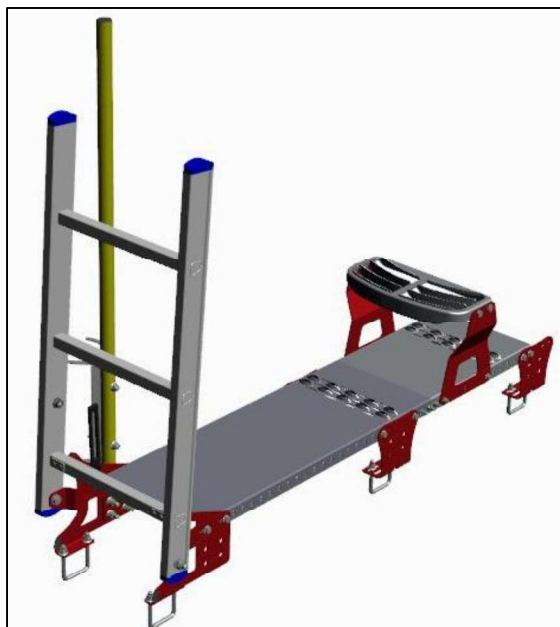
kit de plateforme VS600-1200 avec roues de jauge à l'arrière
